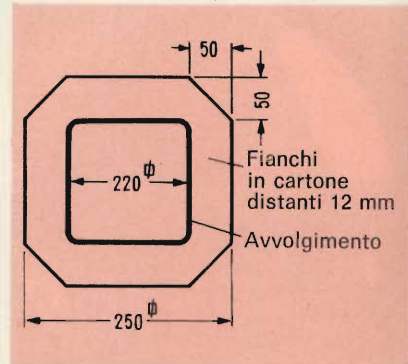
Le dimensioni della carcassa per le due bobine.
